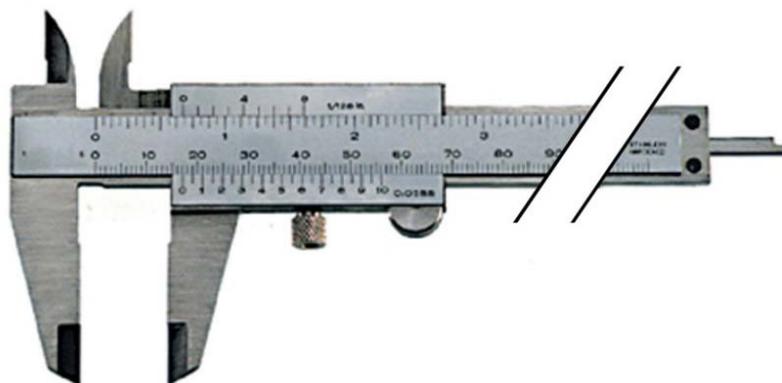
Общий вид штангенциркулей модификации 31006010
